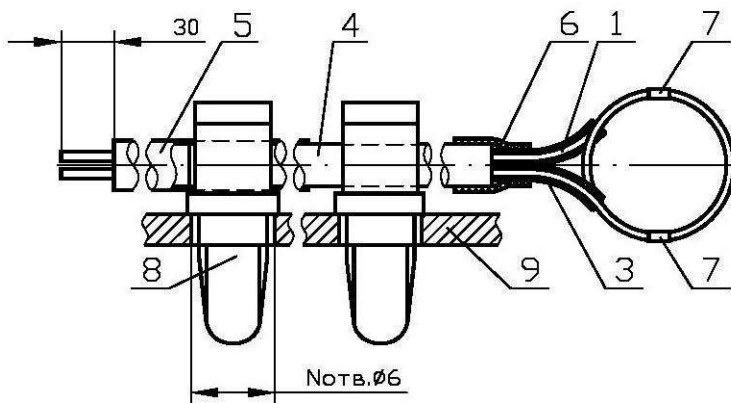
Датчик дуги: 1 – основной световод, 3...5 – защитная оболочка световодов, 6 – термоусадочная трубка, 7 – место установки хомутиков (клипс) для фиксации приёмного кольца, 8 – клипсы, 9 – стенка, перегородка ячейки.
